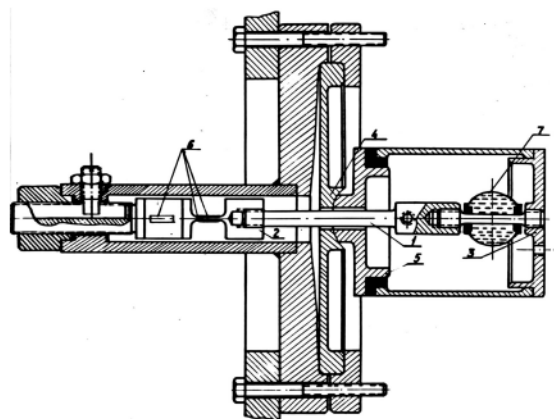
Нагружающее устройство: 1 – переходник; 2 – винтовой захват; 3 – неподвижная опора; 4 – упругий элемент; 5 – сферическая опора; 6 – тензодатчики проволоочные; 7 – баллон с агрессивной средой
